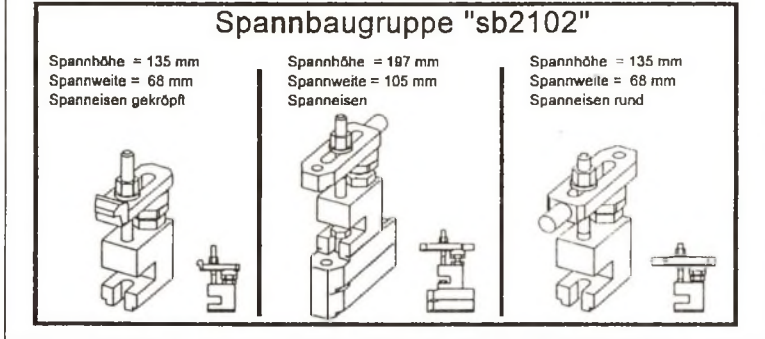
Handling komplexer Objektstrukturen (Baugruppen)
